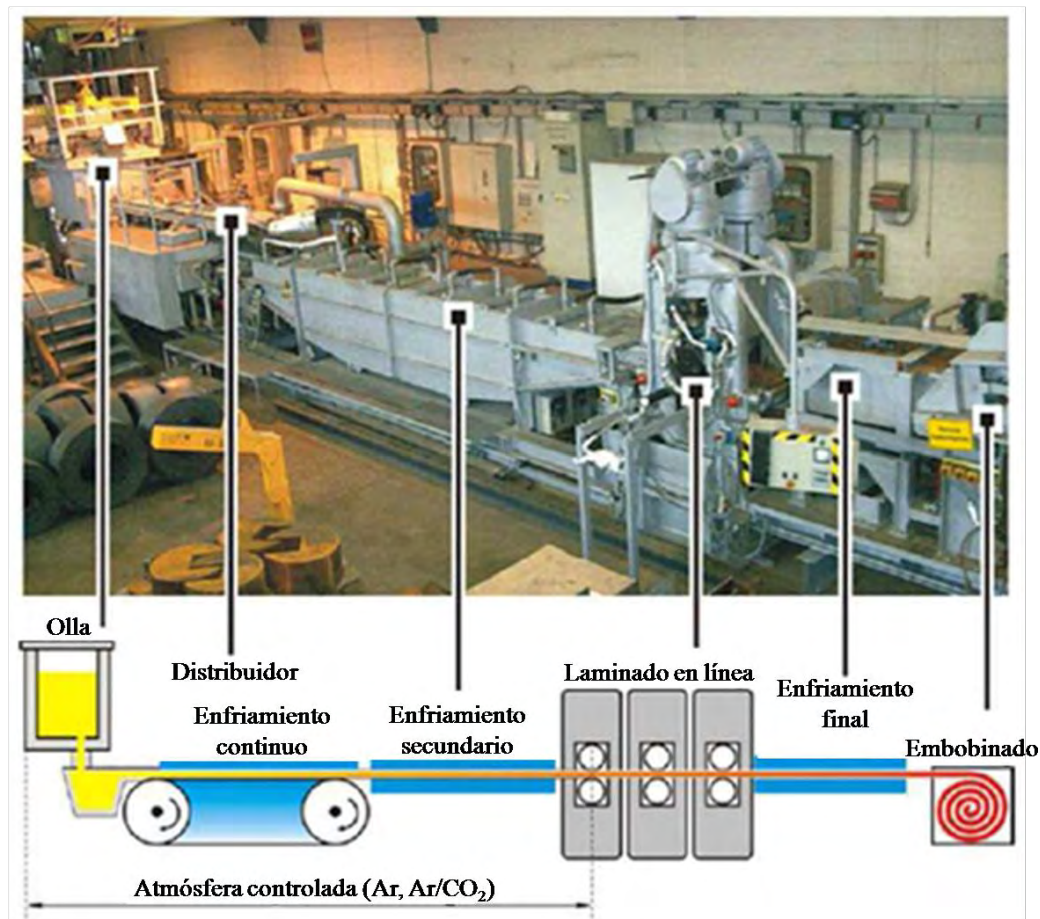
Planta piloto de producción de acero TWIP [52].
